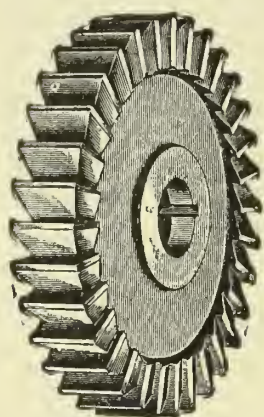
Engzahniger Scheibenfräser mit gefrästen Zähnen, an 3 Flächen schneidend.
